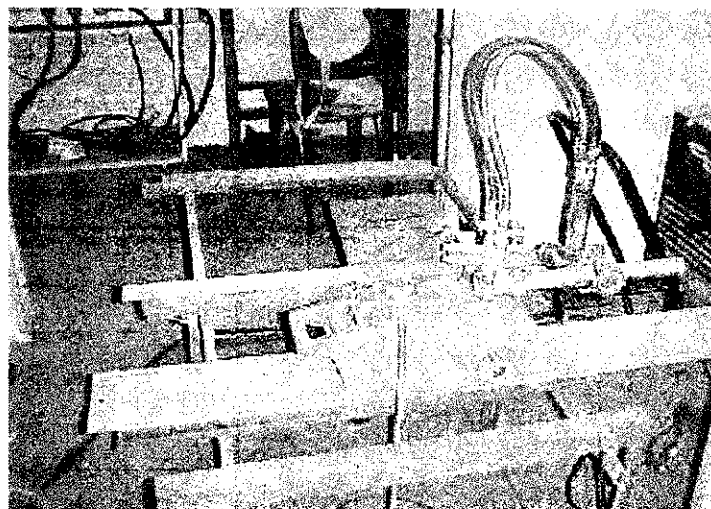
Sistema Desenvolvido para a Automatização do Processo de Soldagem.
